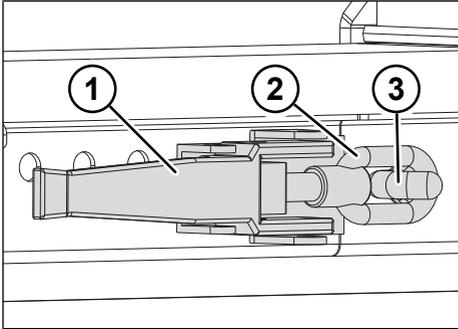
Levier de fermeture sur la poutre d'appui bloqué
